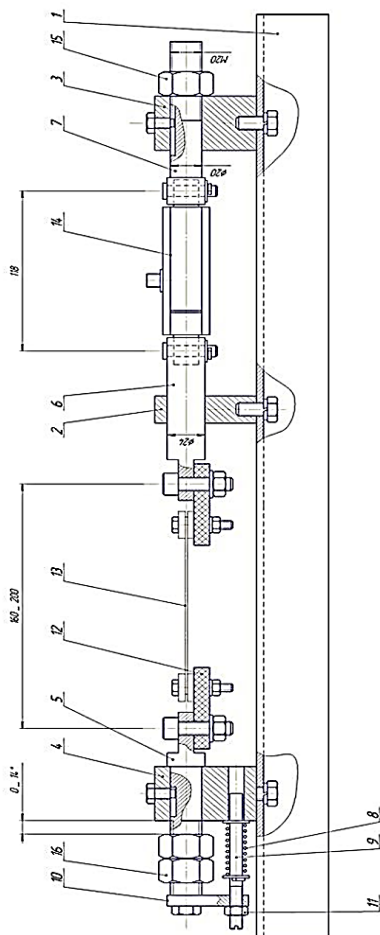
Схема стенда для испытания проволочных силовых элементов:
